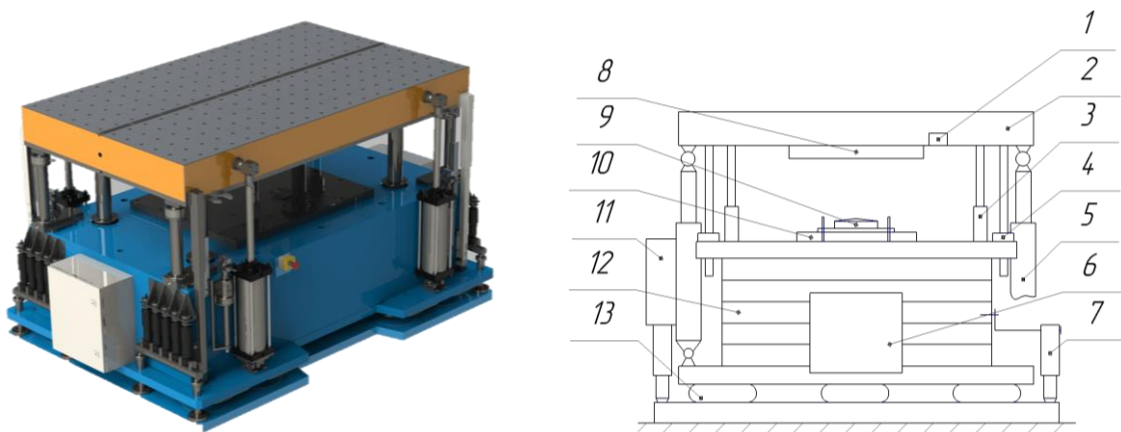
Внешний вид ударной машины стенда СМУ2000 и её компоновочная схема
